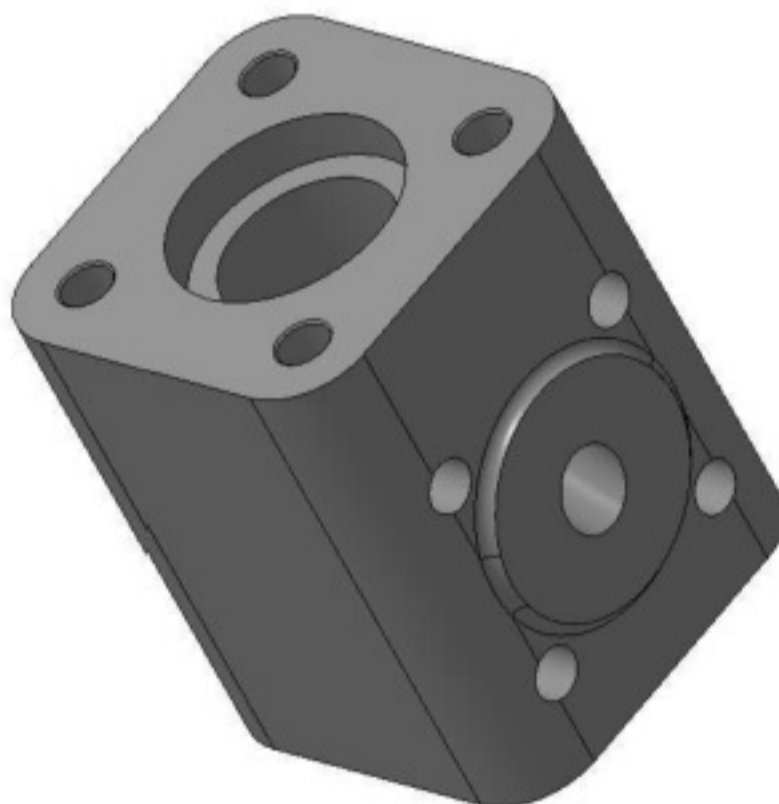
3D-модель деталі «Корпус ГР-004.55.001»
